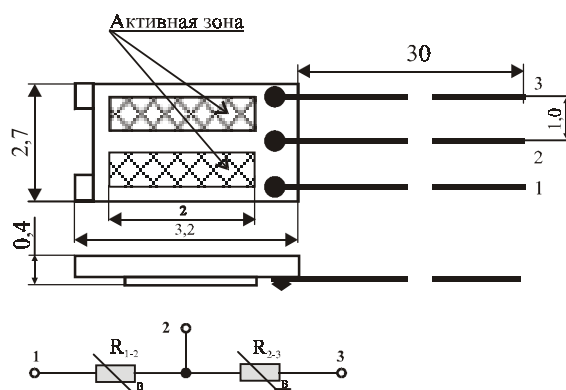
Внешний вид и габаритные размеры магниторезисторов FP 110 D 155; FP 110 L 60, FP 111 L 100
